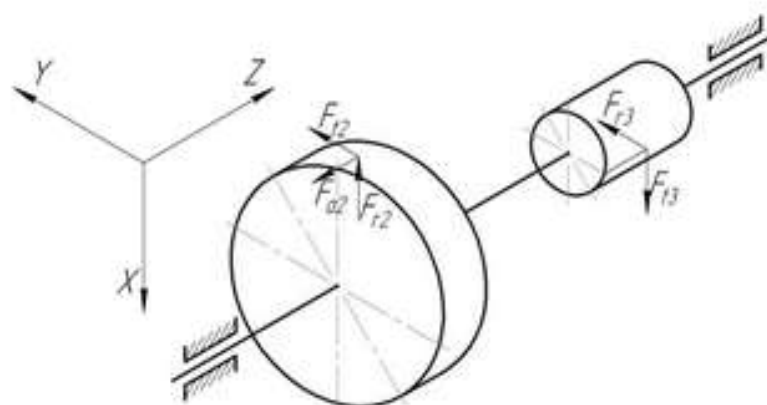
Силова схема тихохідного вала черв'ячної передачі
